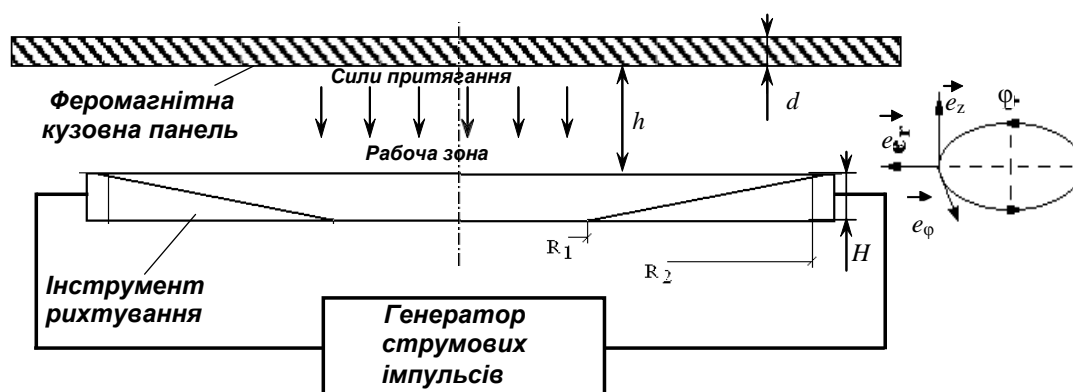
Розрахункова модель інструменту з внутрішнім отвором конічного профілю
